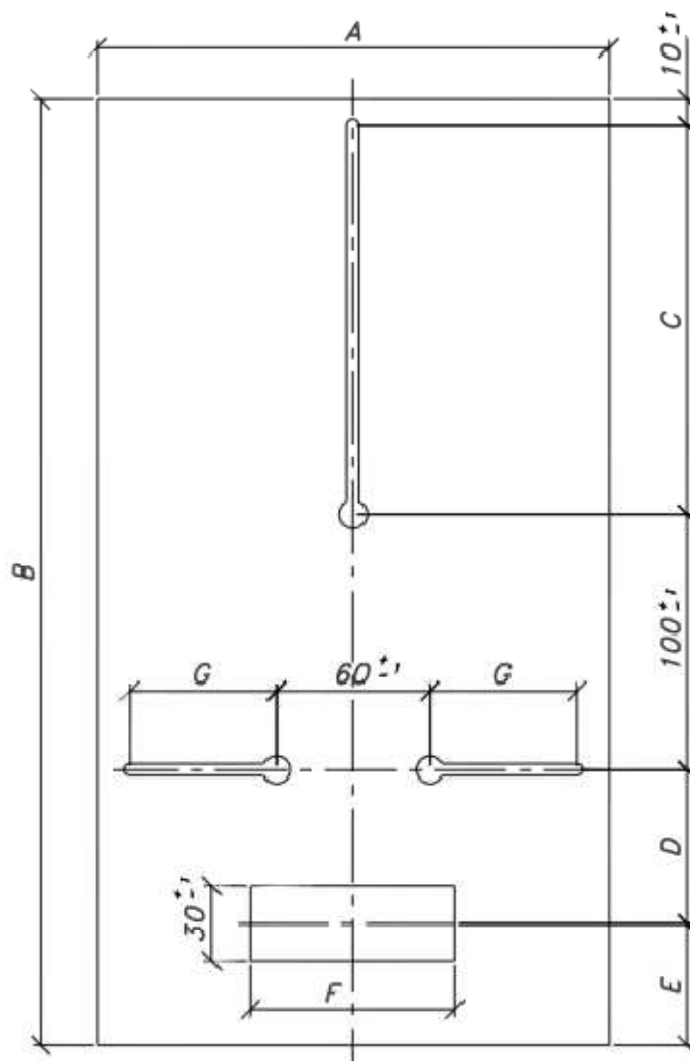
Panel de montaje de contadores. Dimensiones en mm
